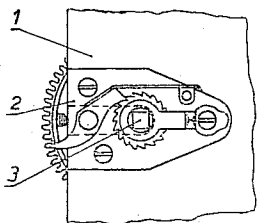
Inny rodzaj dzielonego wałka sprężyny.
